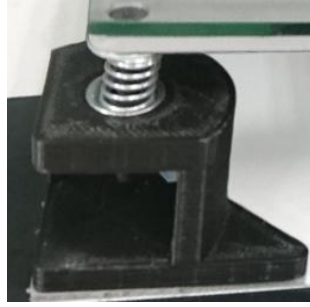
Conjunto ensamblado de un soporte de la base de impresión.
